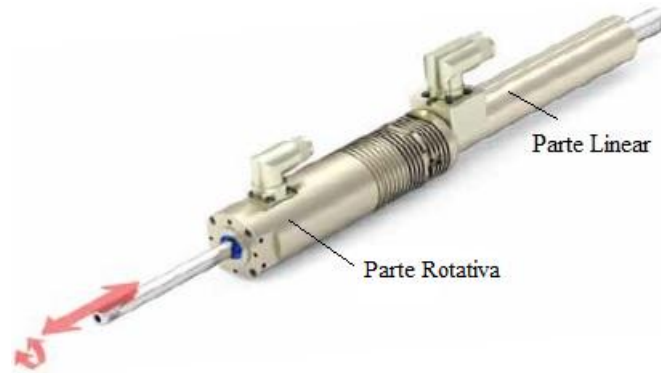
Máquina linear e rotativa (modificado de [7]).
